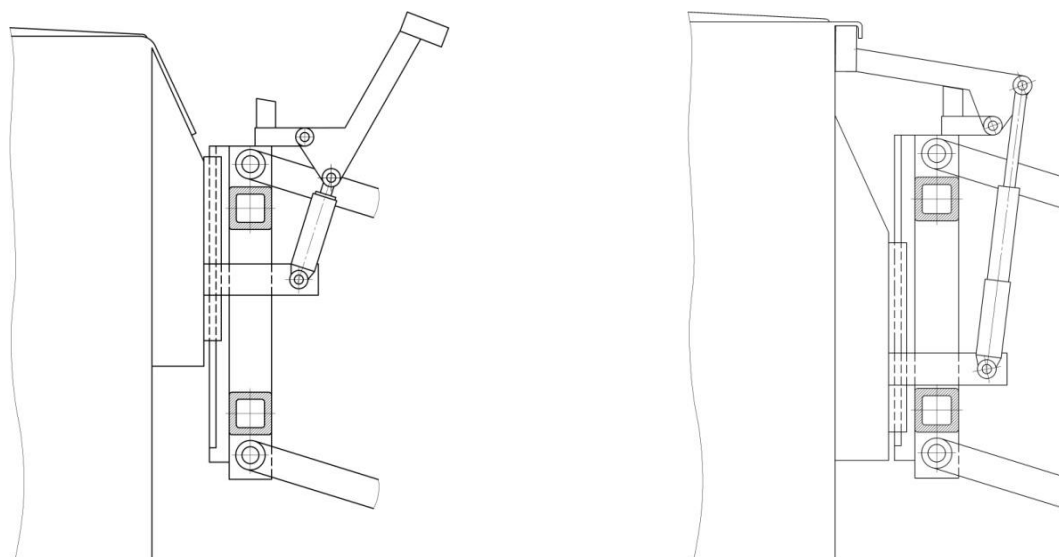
Подъемно-опрокидывающее устройство для контейнеров с различными захватывающими приспособлениями (разработано авторами на основе патента RU2107014)
